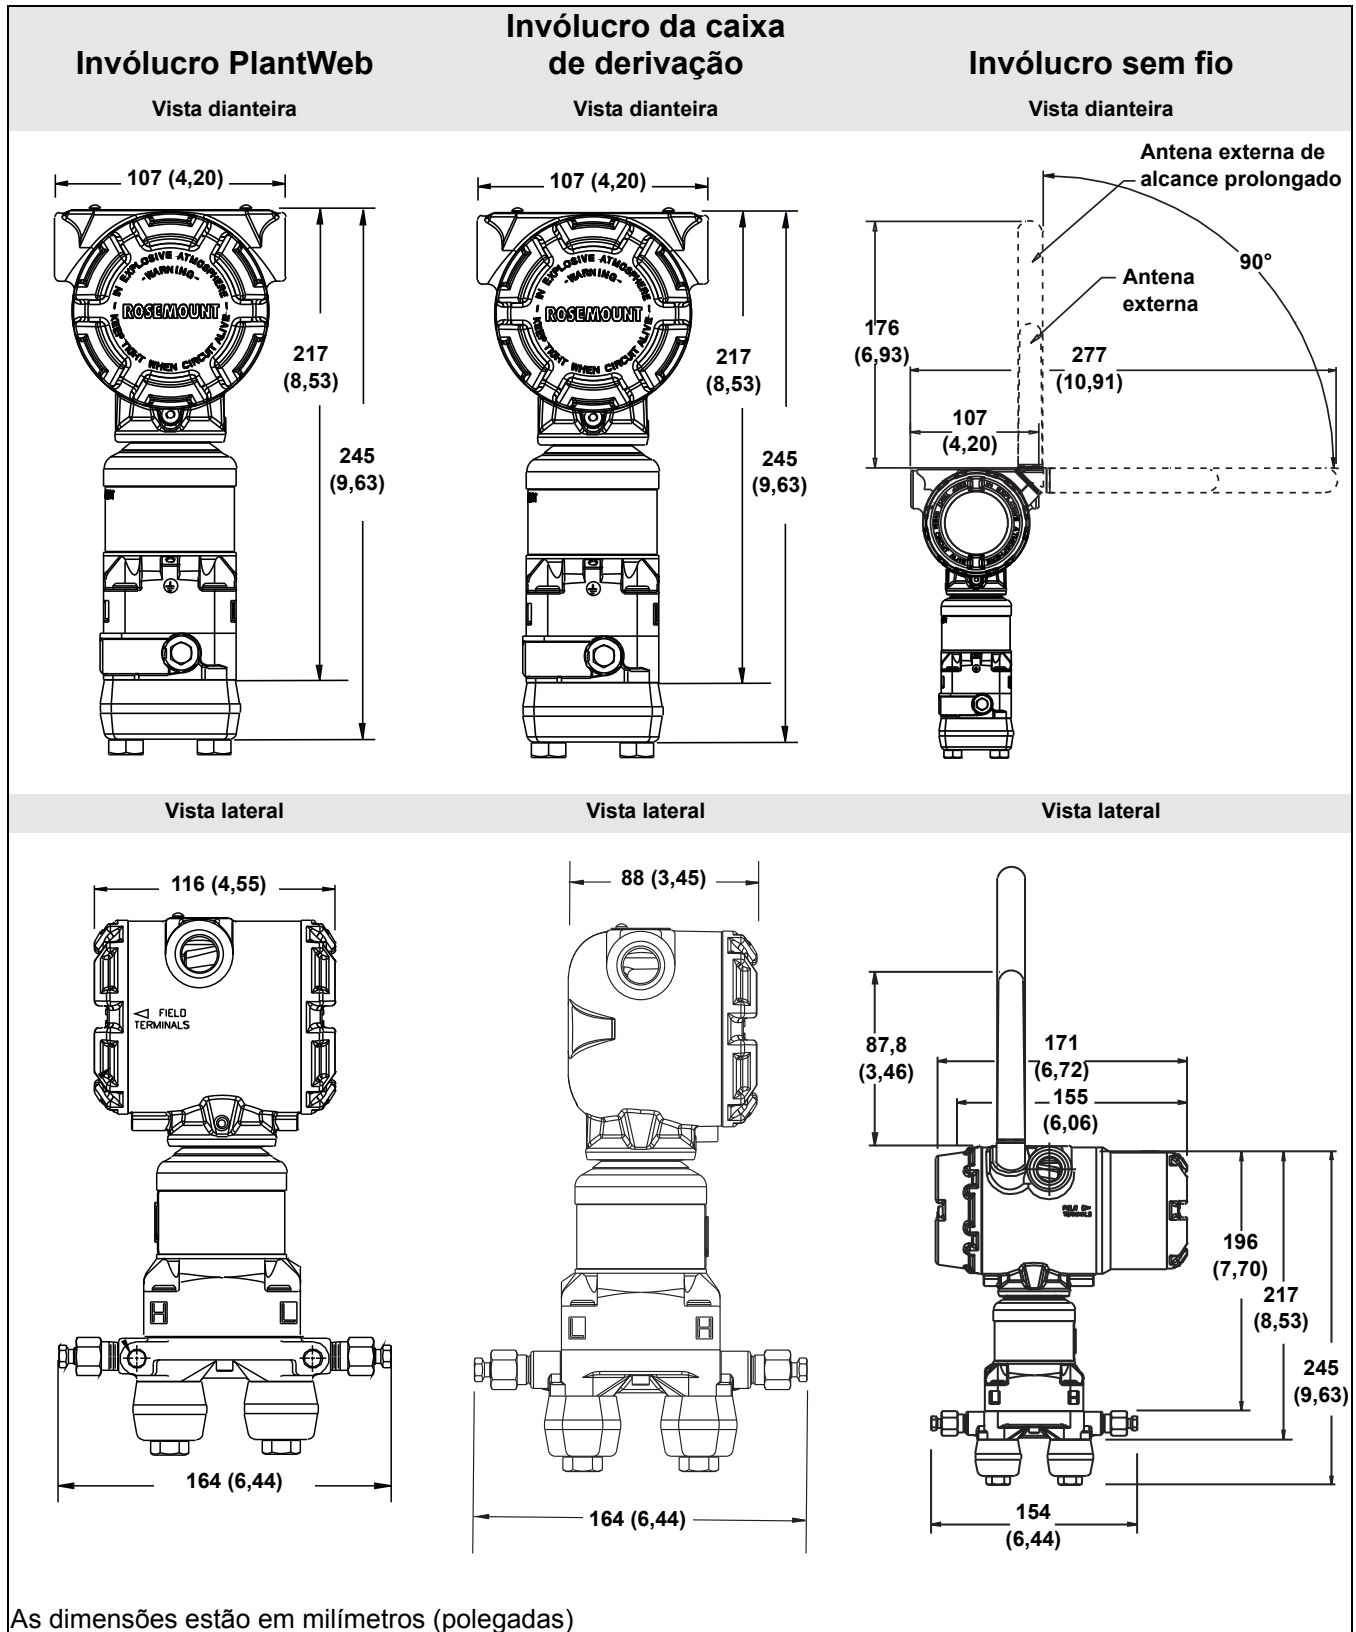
Transmissor com módulo e flange tradicional de sensor coplanar
